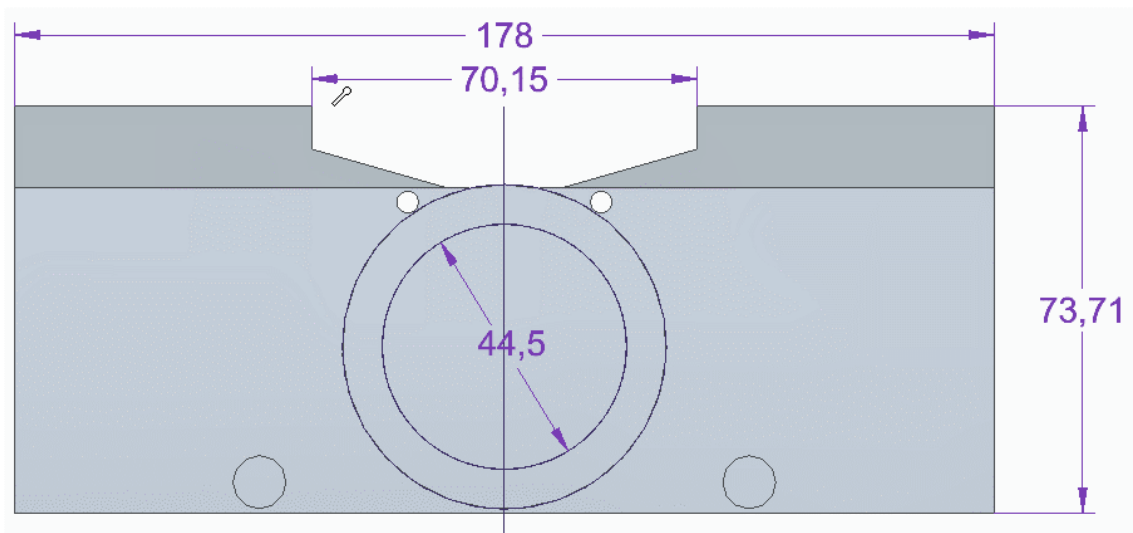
Alzado de la pieza base. Fuente: elaboración propia
